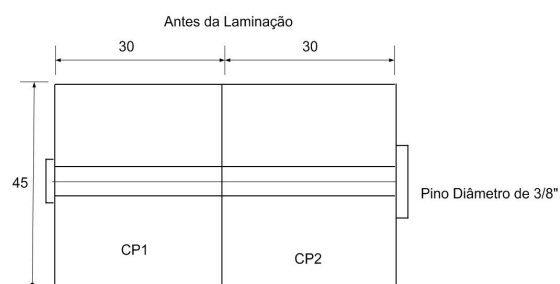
Dimensionamento do corpo de prova (Visão Frontal)
